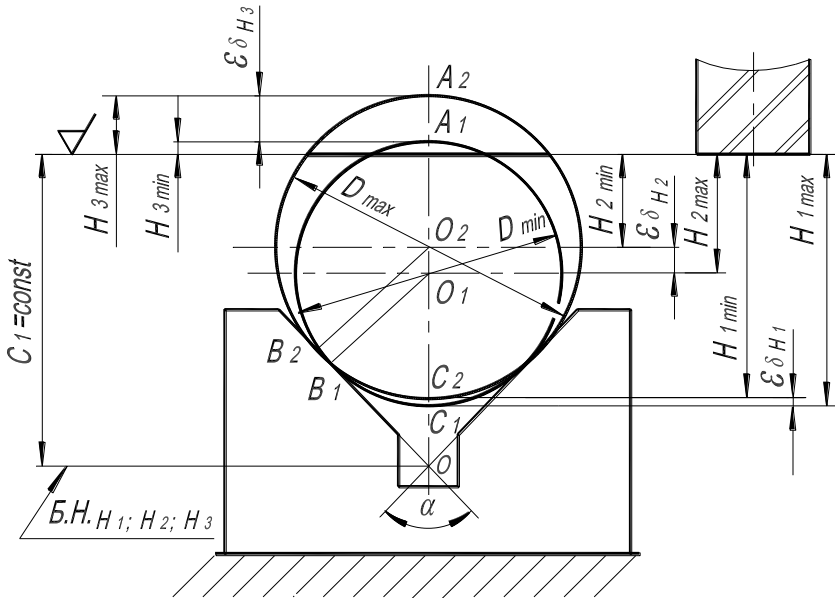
Схема установки заготовки типу «валик» на призму
